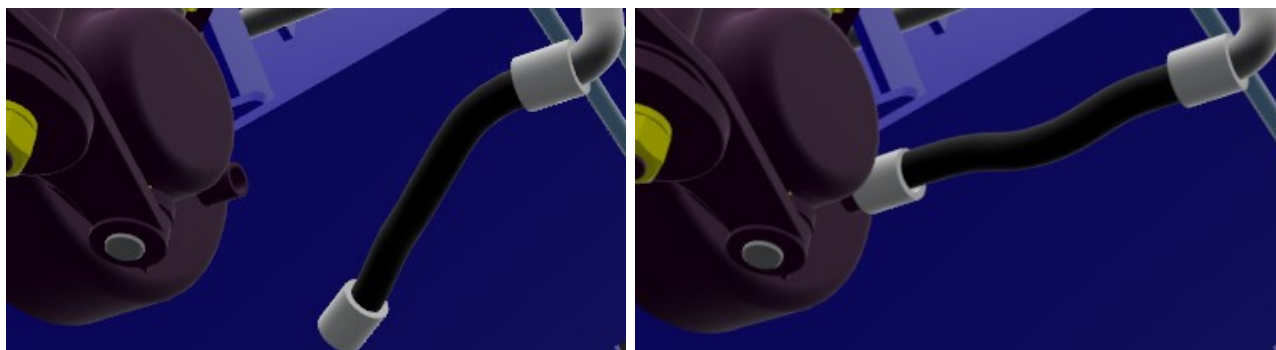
Vizualizace 3D ovladačů; zdroj: autor
